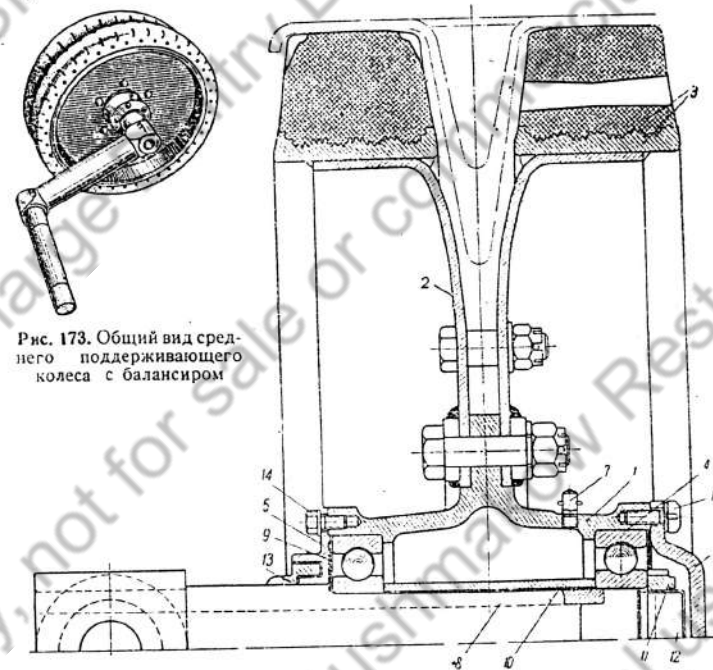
Общий вид среднего поддерживающего колеса с балансиром
